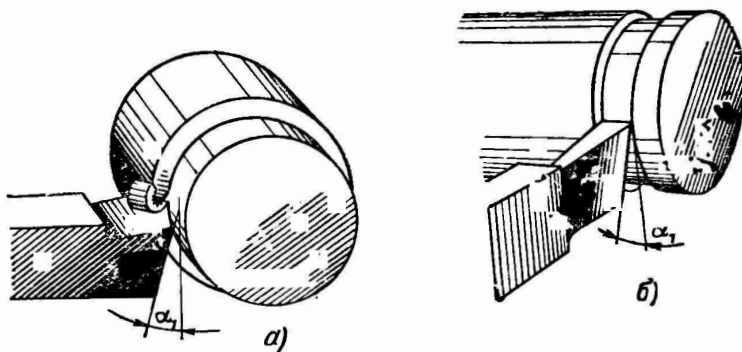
Задний вспомогательный угол проходного и отрезного резцов
